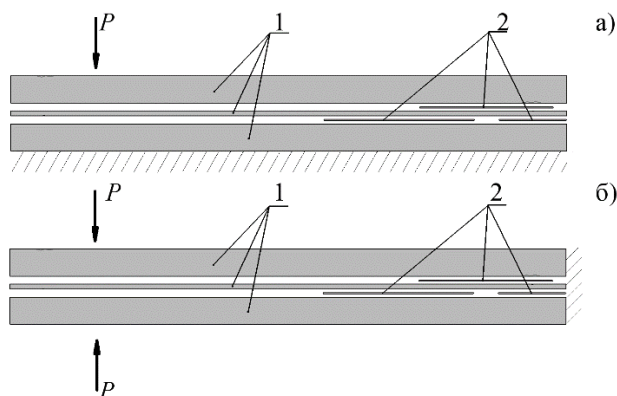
Схема расположения листовых заготовок и ПСП. Цифрами обозначены:
